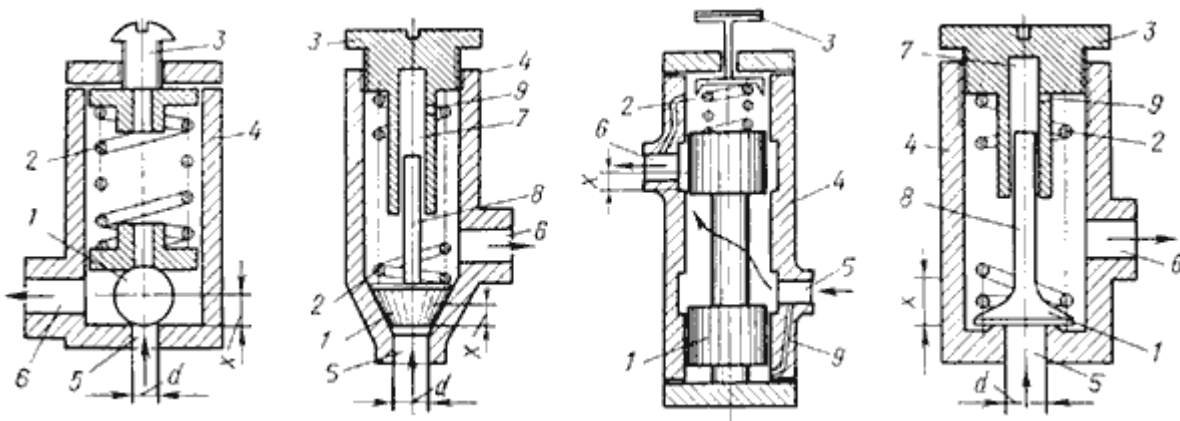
Принципиальные схемы напорных клапанов с запорно-регулирующими элементами: а - с шариковым; б - с конусным; в - с золотниковым; г - с тарельчатым.
